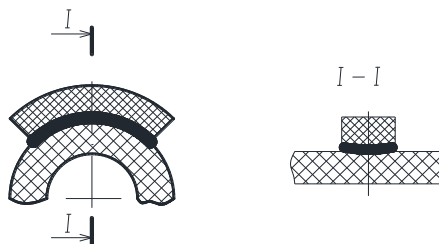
Конструктивные элементы шва сварного соединения (шов НЗ)
